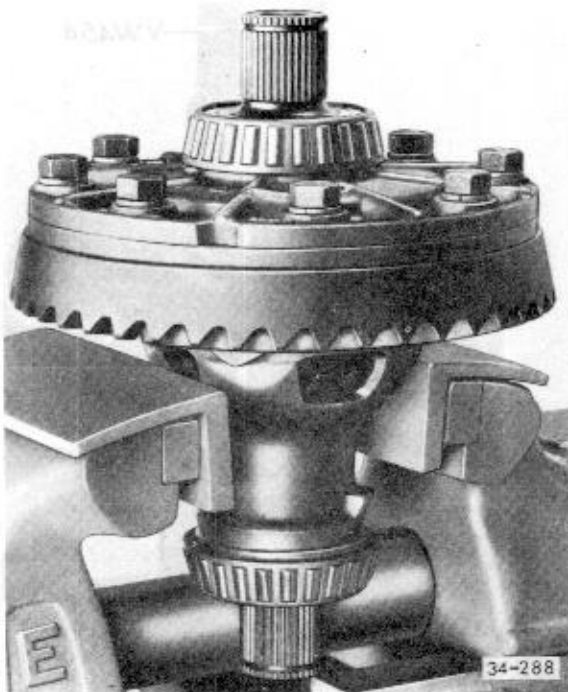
Ausgleichgetriebe in den Schraubstock spannen
